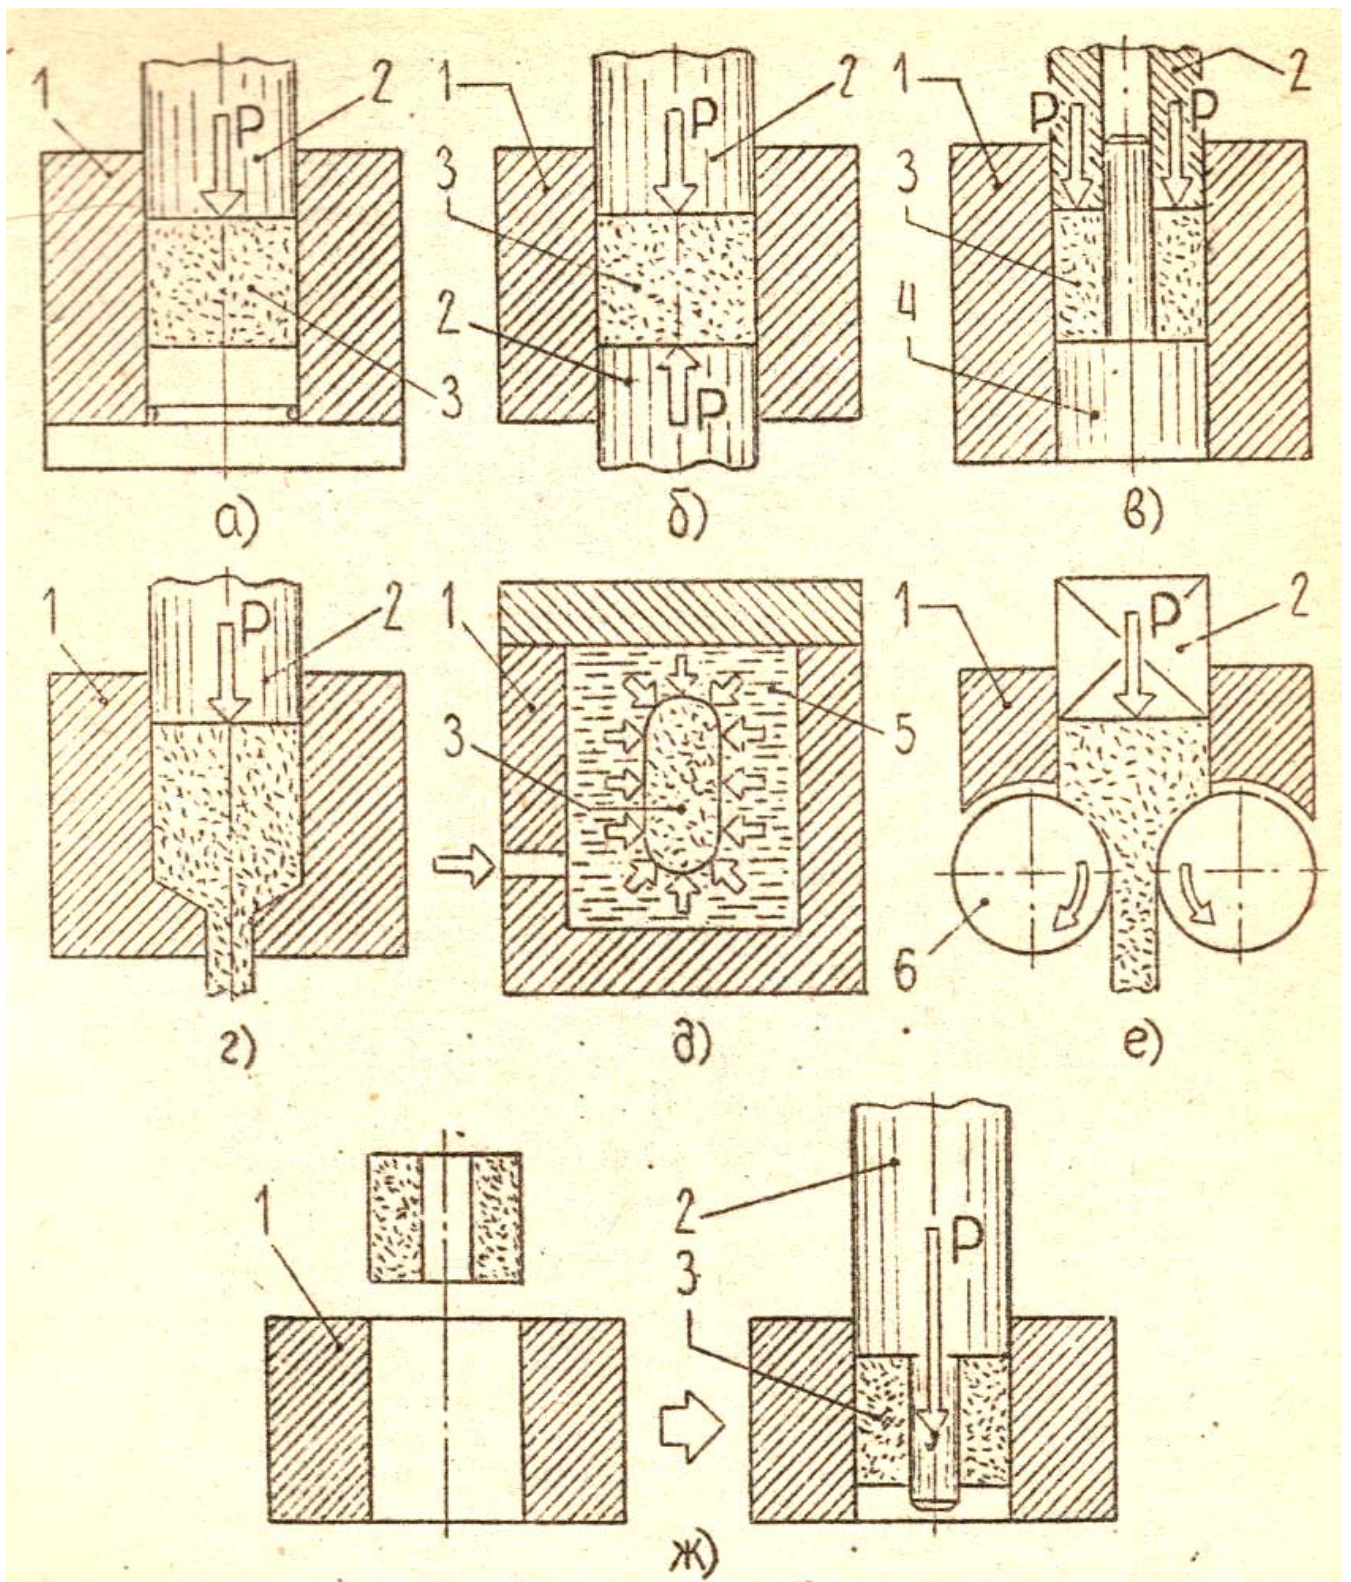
Схема прессования и калибровки изделий из порошков:
